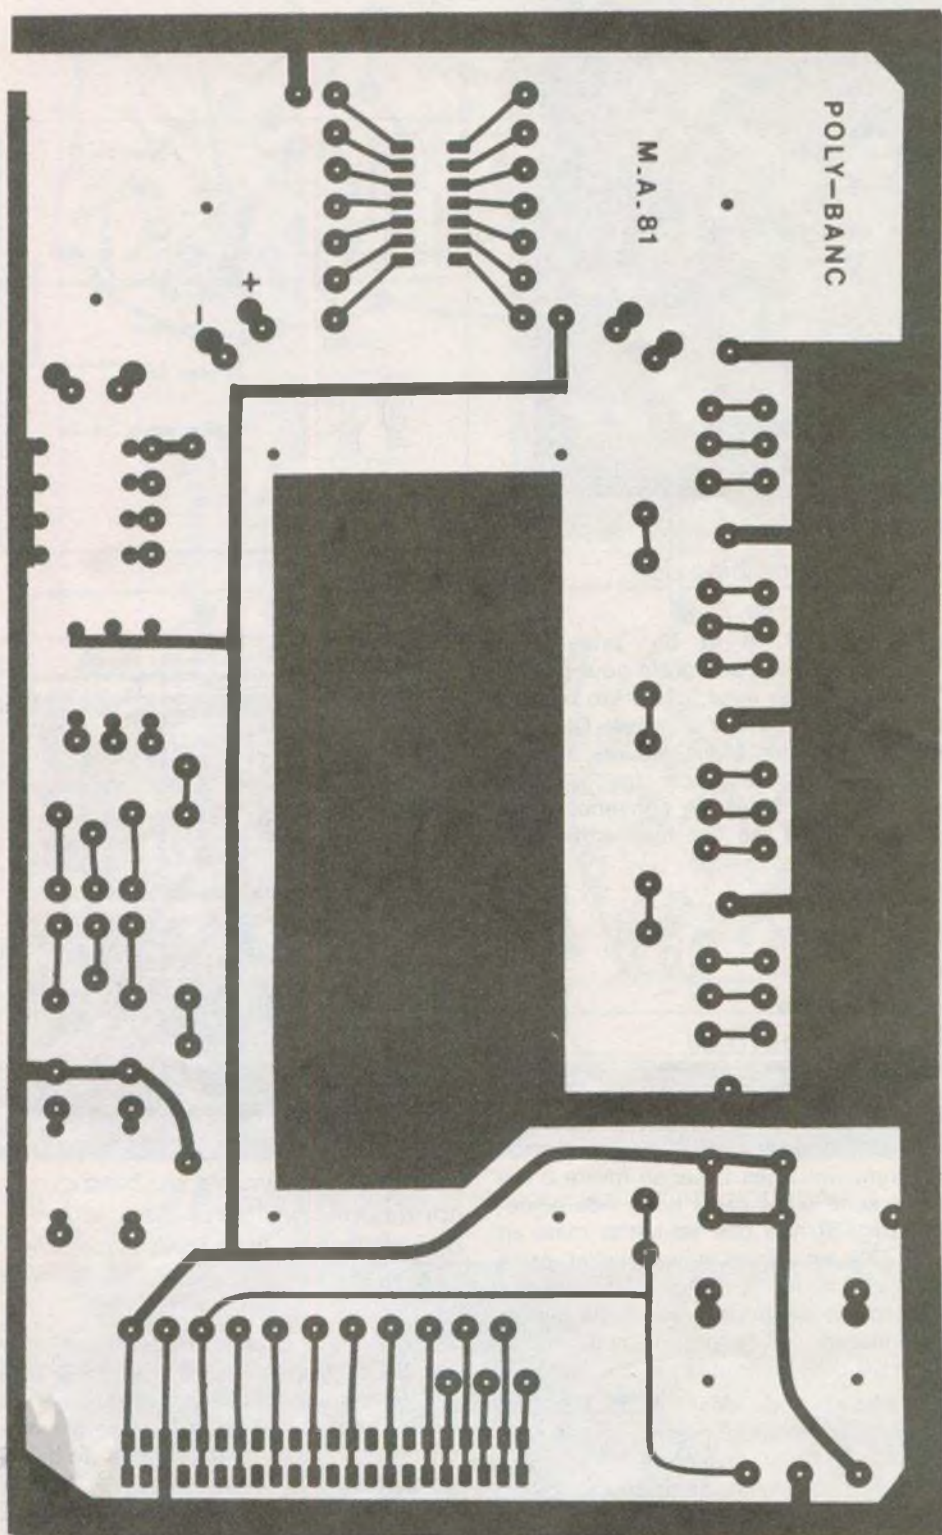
A et 1B. - C'est grand, mais facile à reproduire épouse les dimensions d'un couvercle en aluminium plaquelette univert
